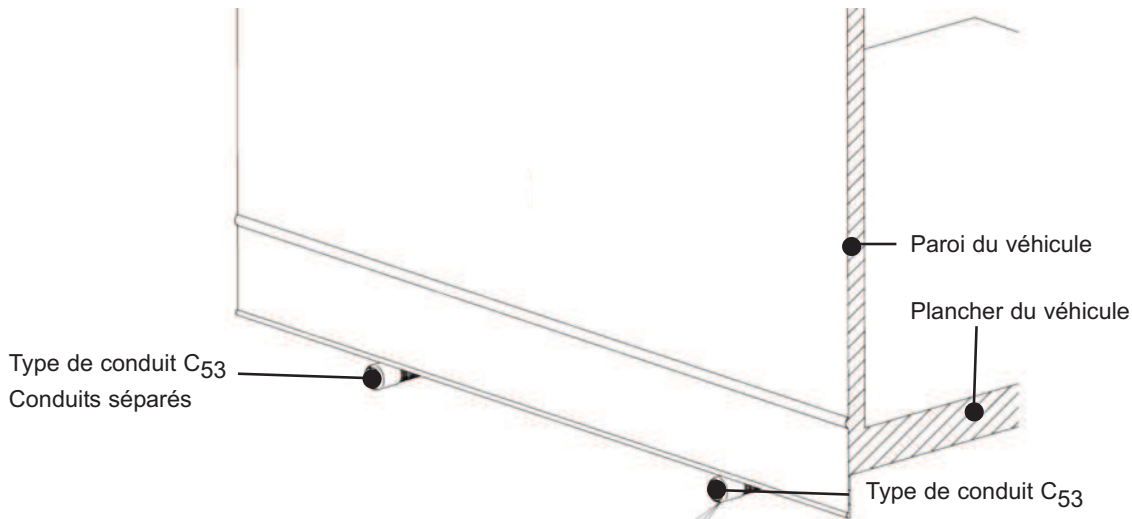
Type de conduit pour l'installation standard C<sub>53</sub>
